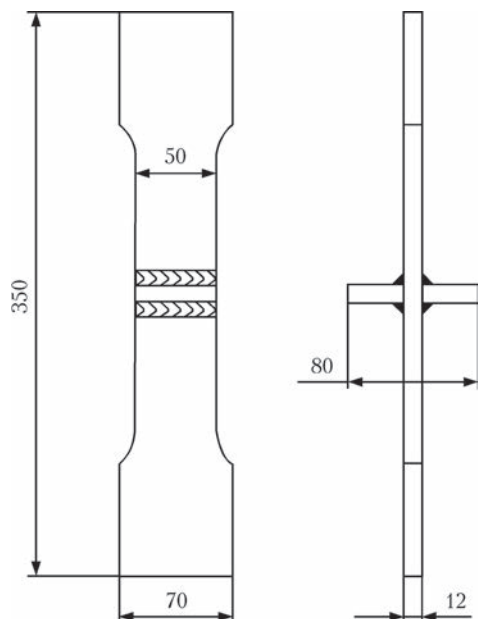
Форма и геометрические размеры образца таврового сварного соединения
